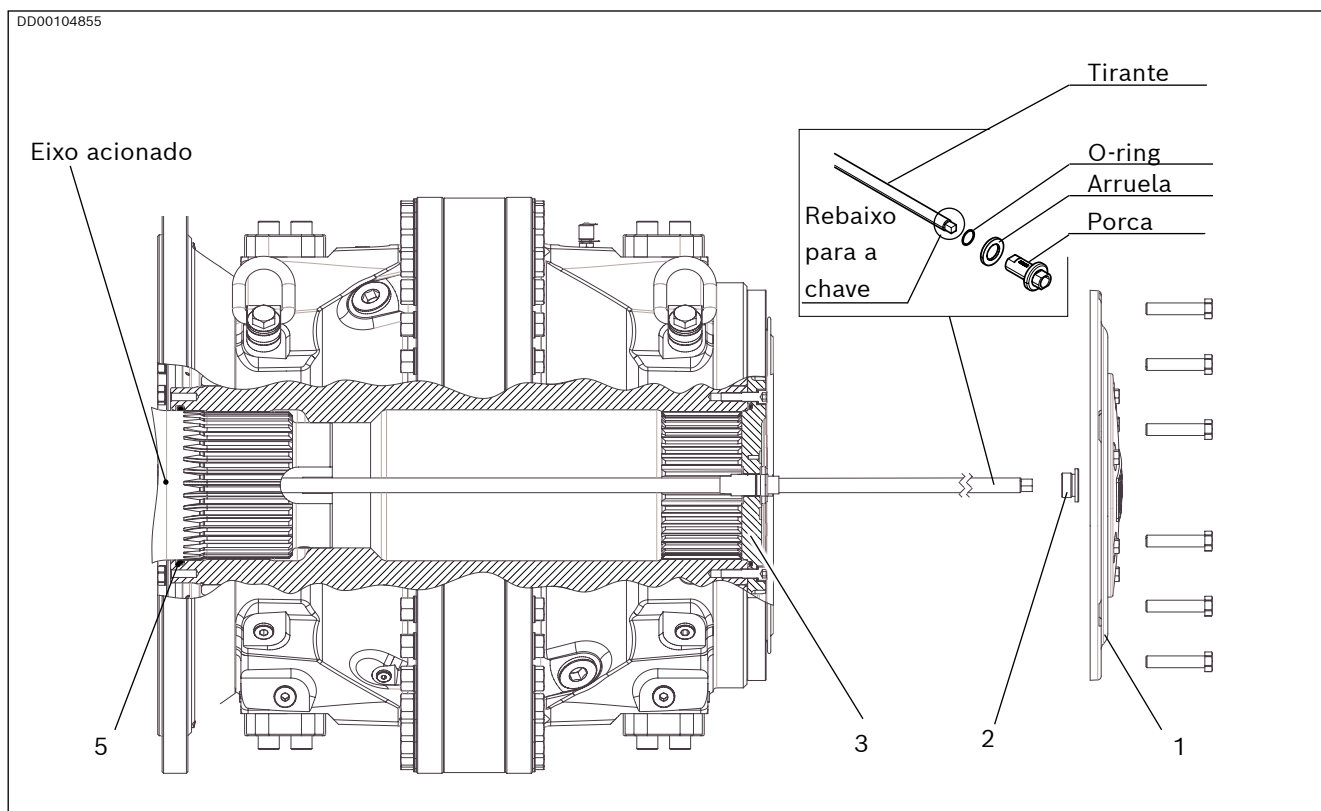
Montagem do motor com estria com a ferramenta de montagem
